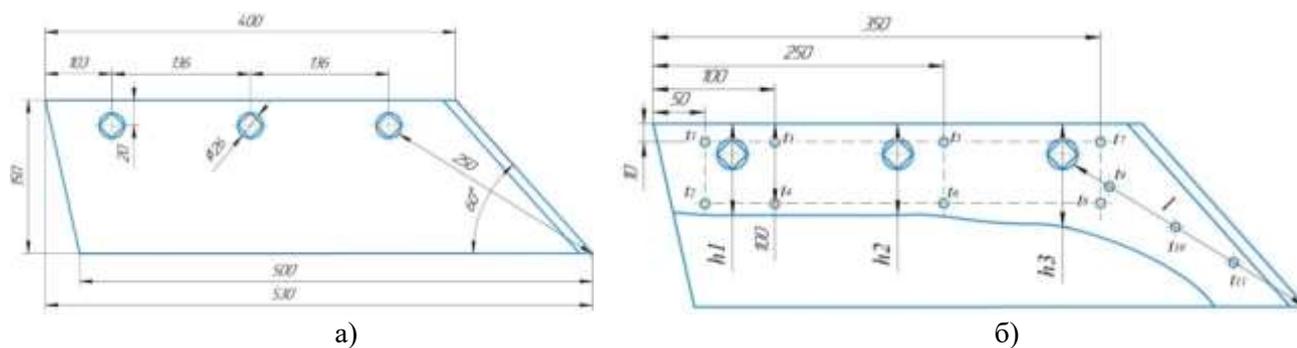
Изучаемая деталь (а - чертеж ; б – схема измерения ножа)
